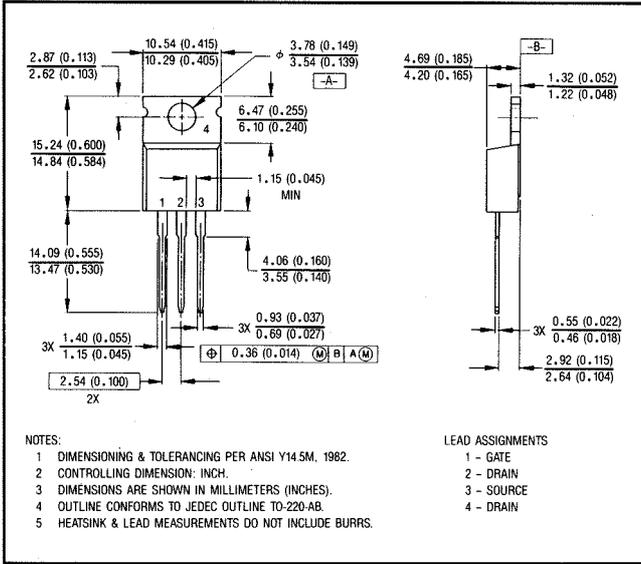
Стандартный пластмассовый корпус TO-220 AB
